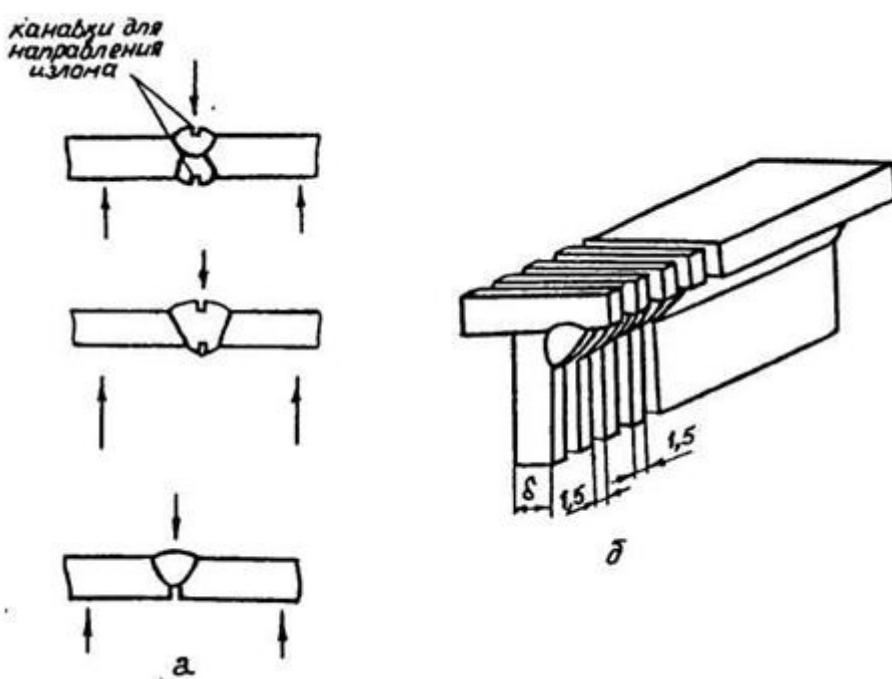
Вскрытие сварных швов изломом и фрезерованием (б)
